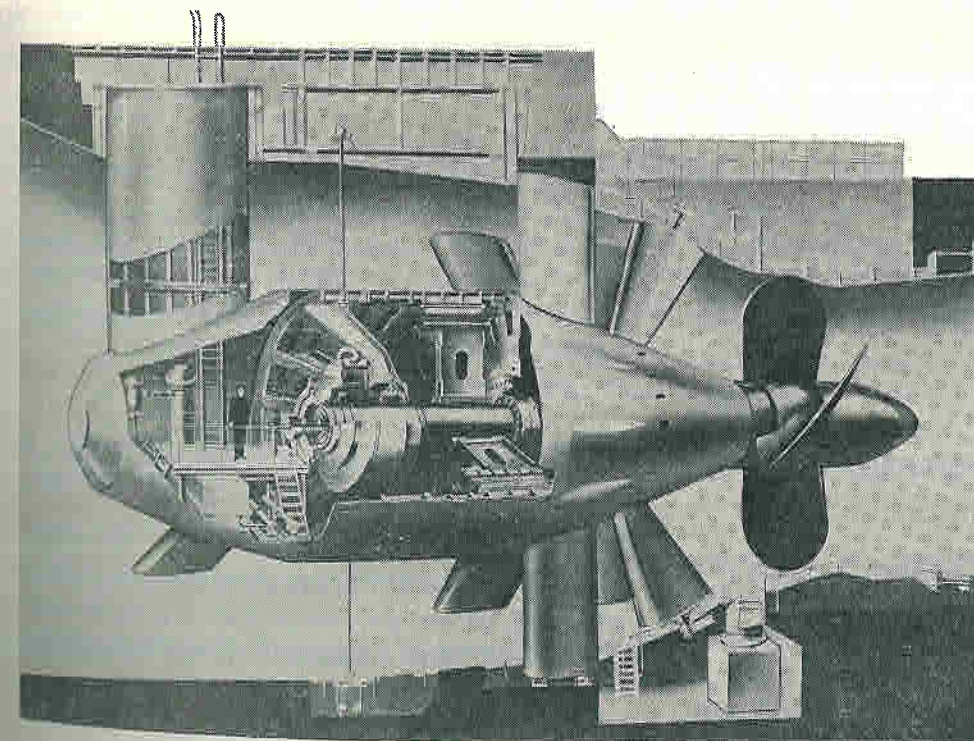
Двухшaftный горизонтальный капсульный гидроагрегат с диаметром рабочего колеса 6 м и водяным охлаждением обмотки статора и ротора
